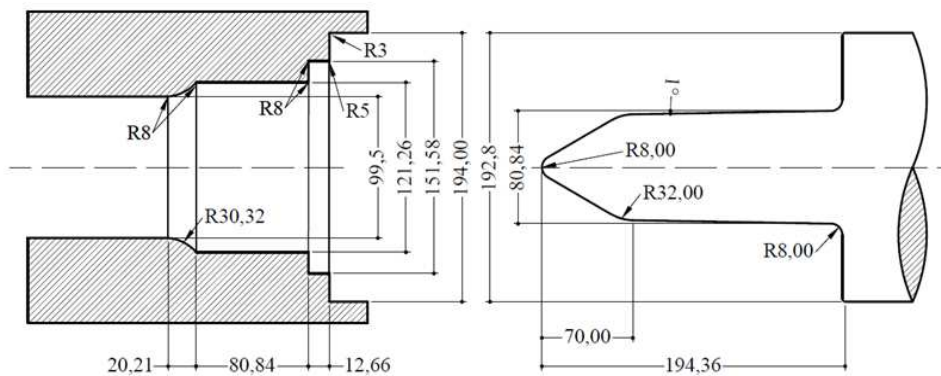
Diseño del anclaje, matriz y punzón de la etapa final de forjado [14].
